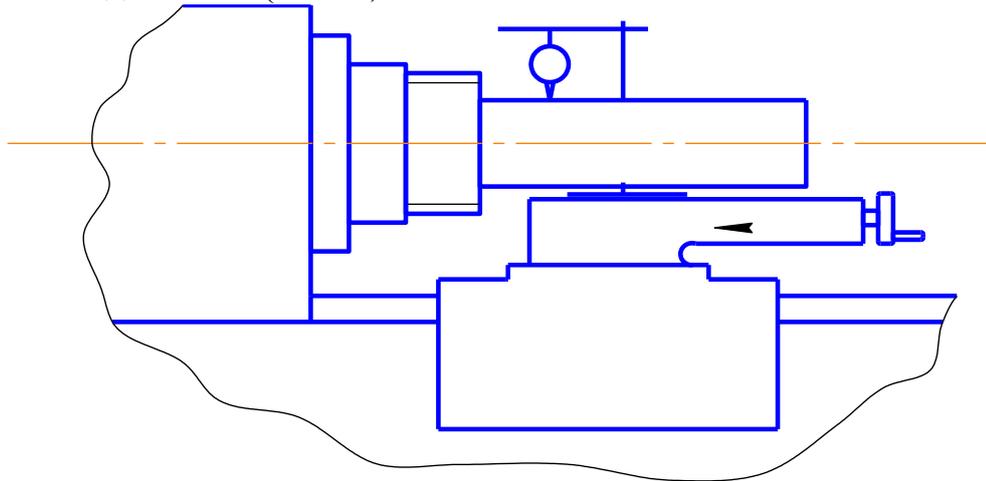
Схема установки индикатора для проверки параллельности направления перемещения салазок суппорта оси шпинделя
